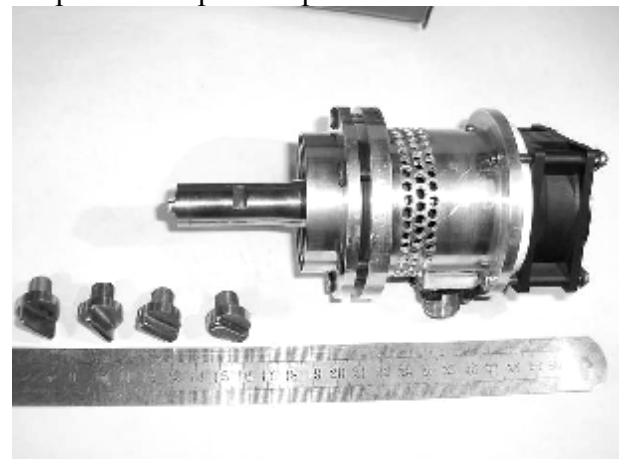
Механический блок и комплект сменных инструментов для сварки и резки ультразвукового комплекса
